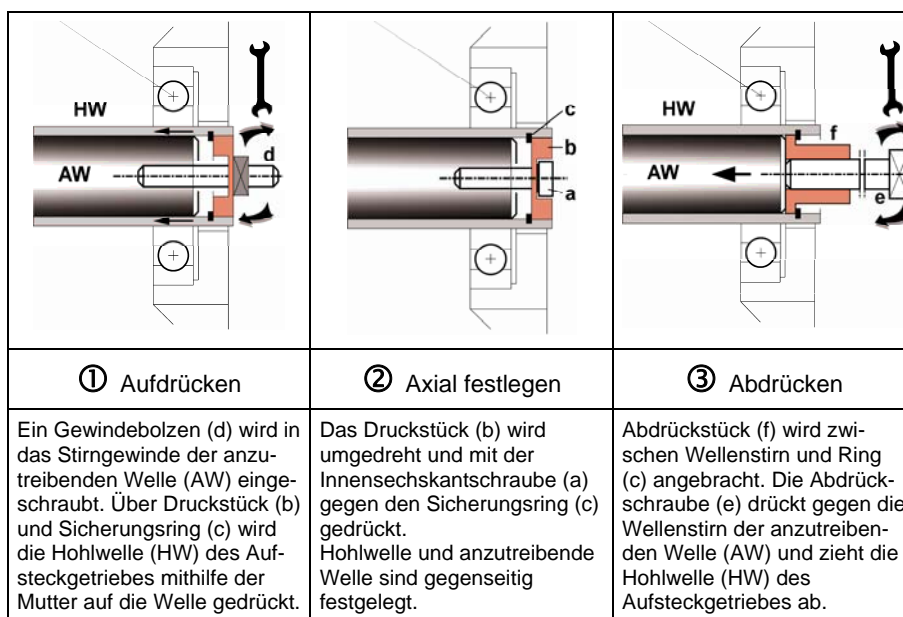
Montagehilfen für Aufsteckgetriebe
